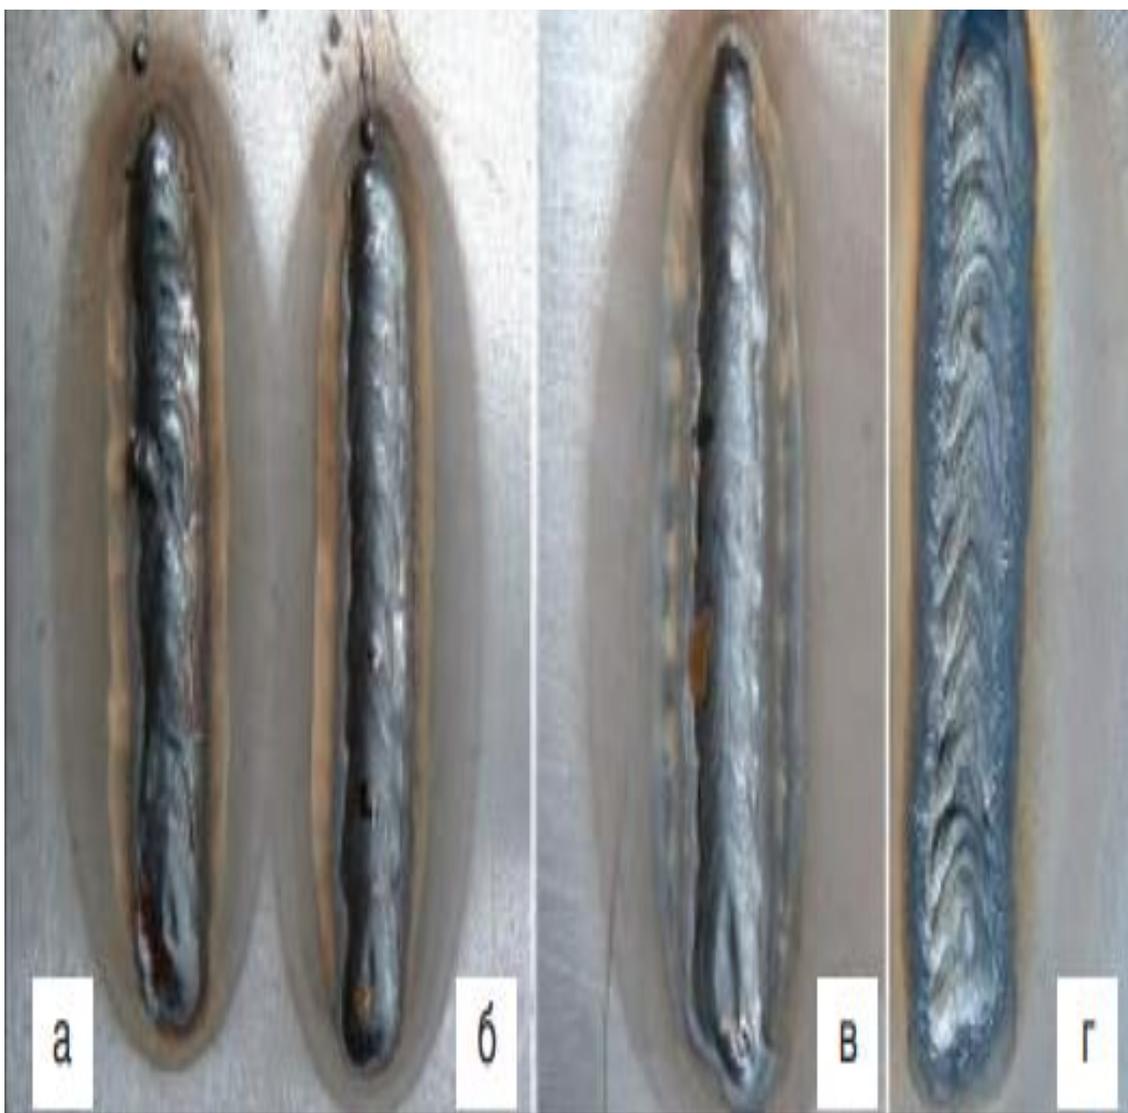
Внешний вид шва, полученного дуговой сваркой в  $\text{CO}_2$
